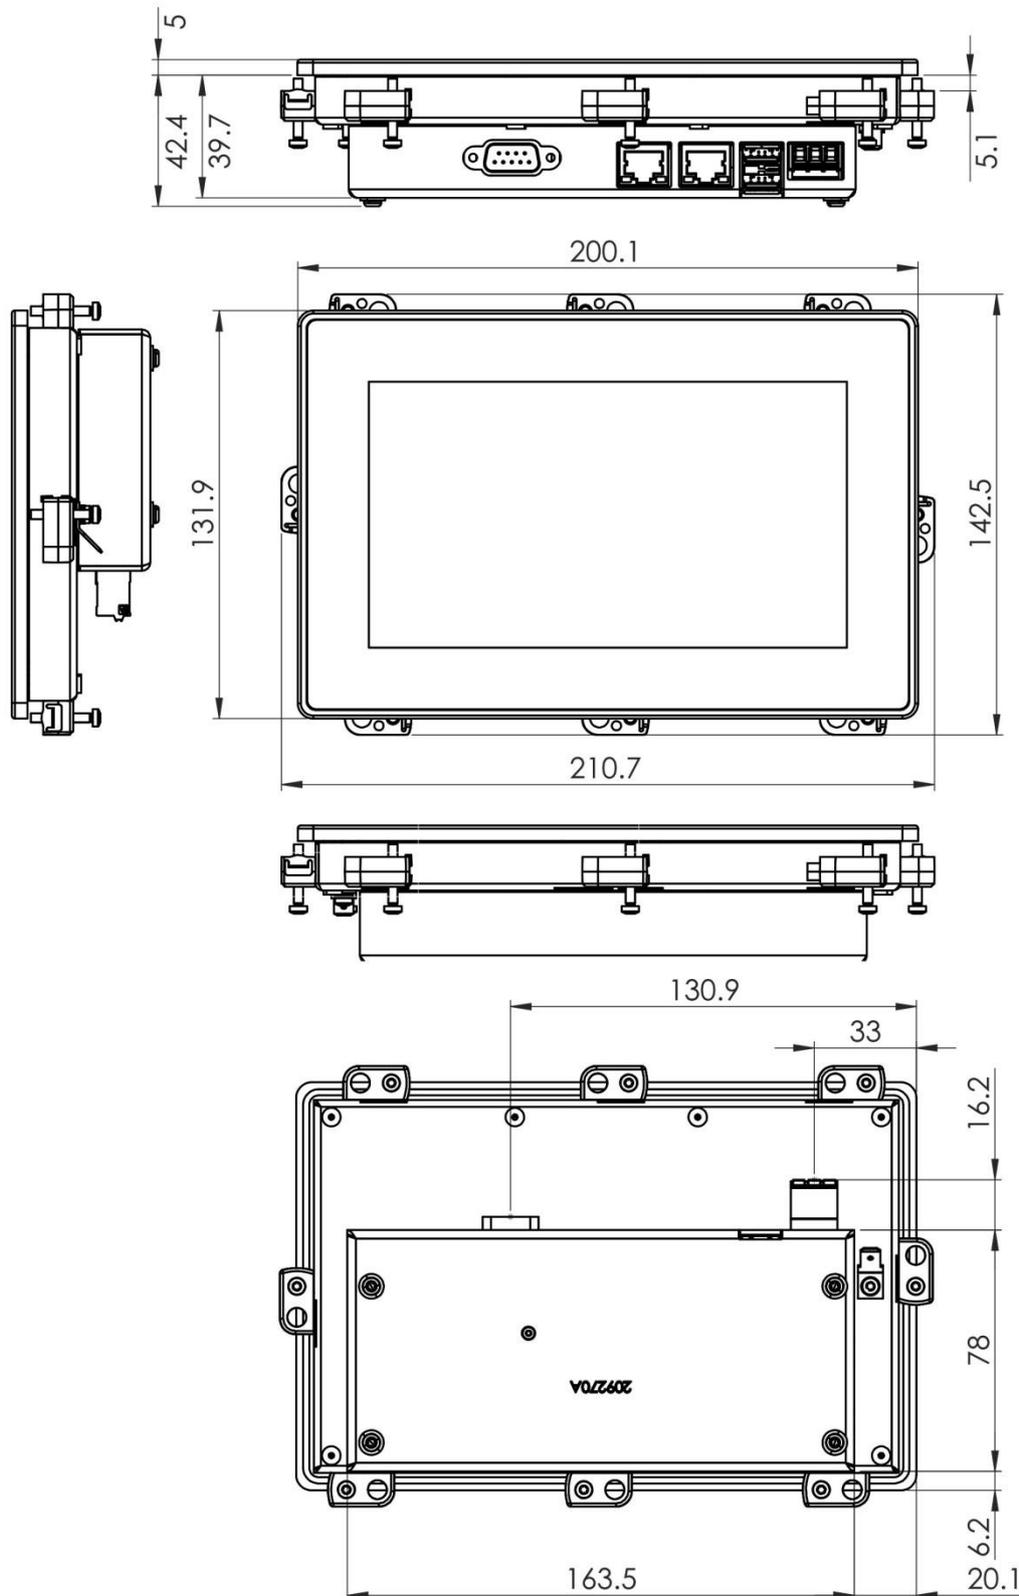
WP-70g 44-12x0 Montage-Ausschnitt
